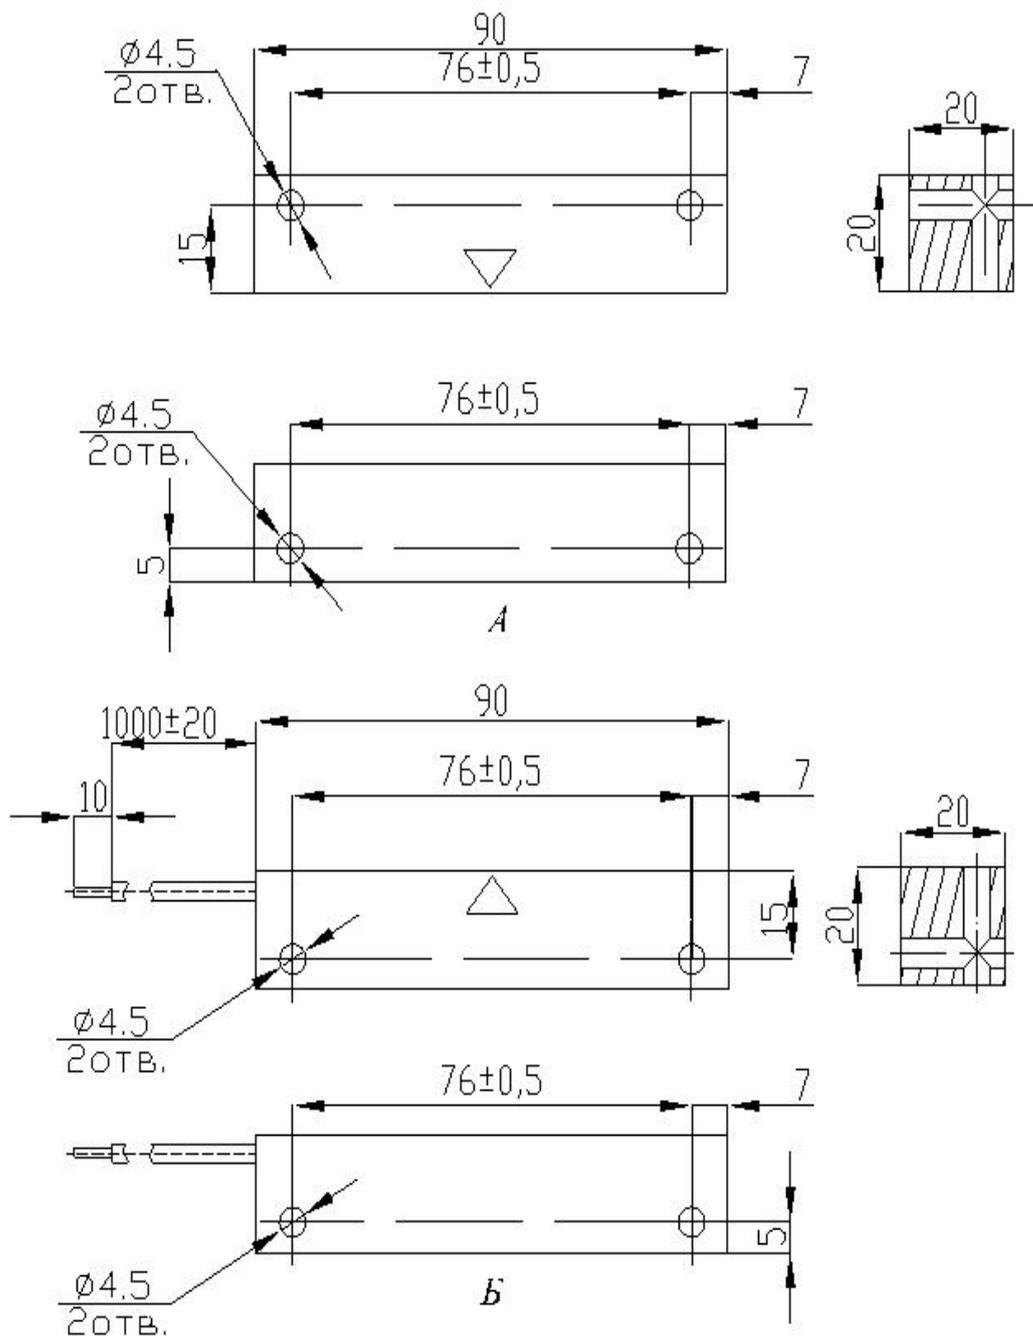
Габаритные и присоединительные размеры датчиков ДИМ-2 (исп. 100, 102, 104, 105). А - блок магнитов, Б - блок геркона.
